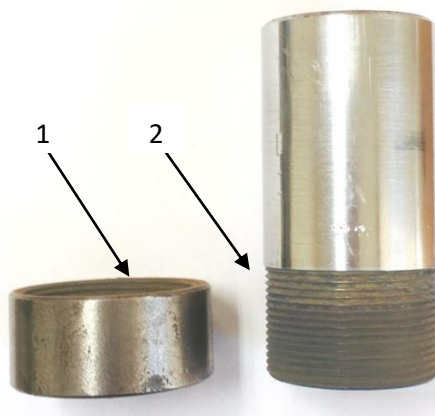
Металлический стакан для фиксации образцов: 1 – дно стакана для установки образца, 2 – цилиндрическая крышка-зажим
